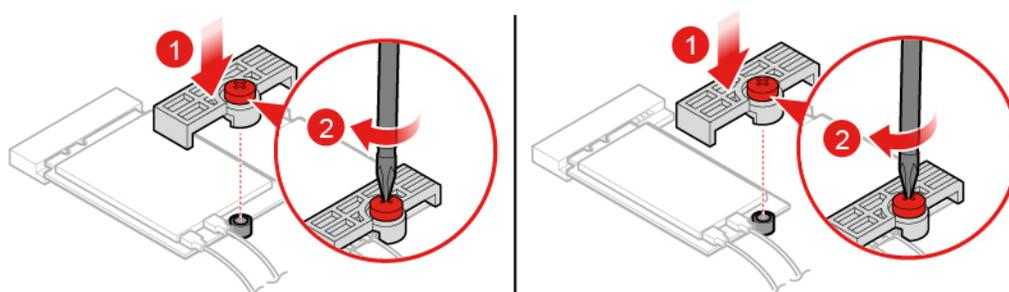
Installation du dispositif de protection de la carte Wi-Fi
